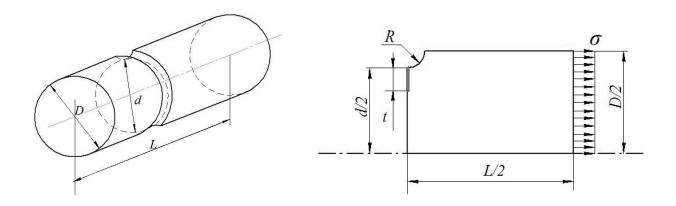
Цилиндрический образец с круговым надрезом полукруглого профиля
